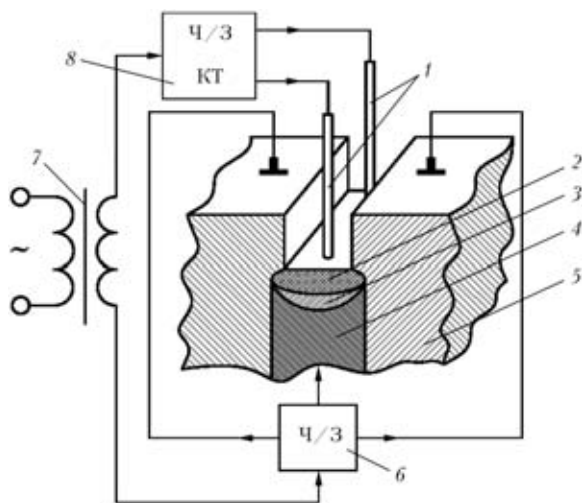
Схема скоростной ЭШС [17]: 1 — электроды; 2 — шлаковая ванна; 3 — металлическая ванна; 4 — сварной шов; 5 — изделие; 6 — трехканальный преобразователь тока; 7 — источник питания; 8 — двухканальный коммутатор тока
